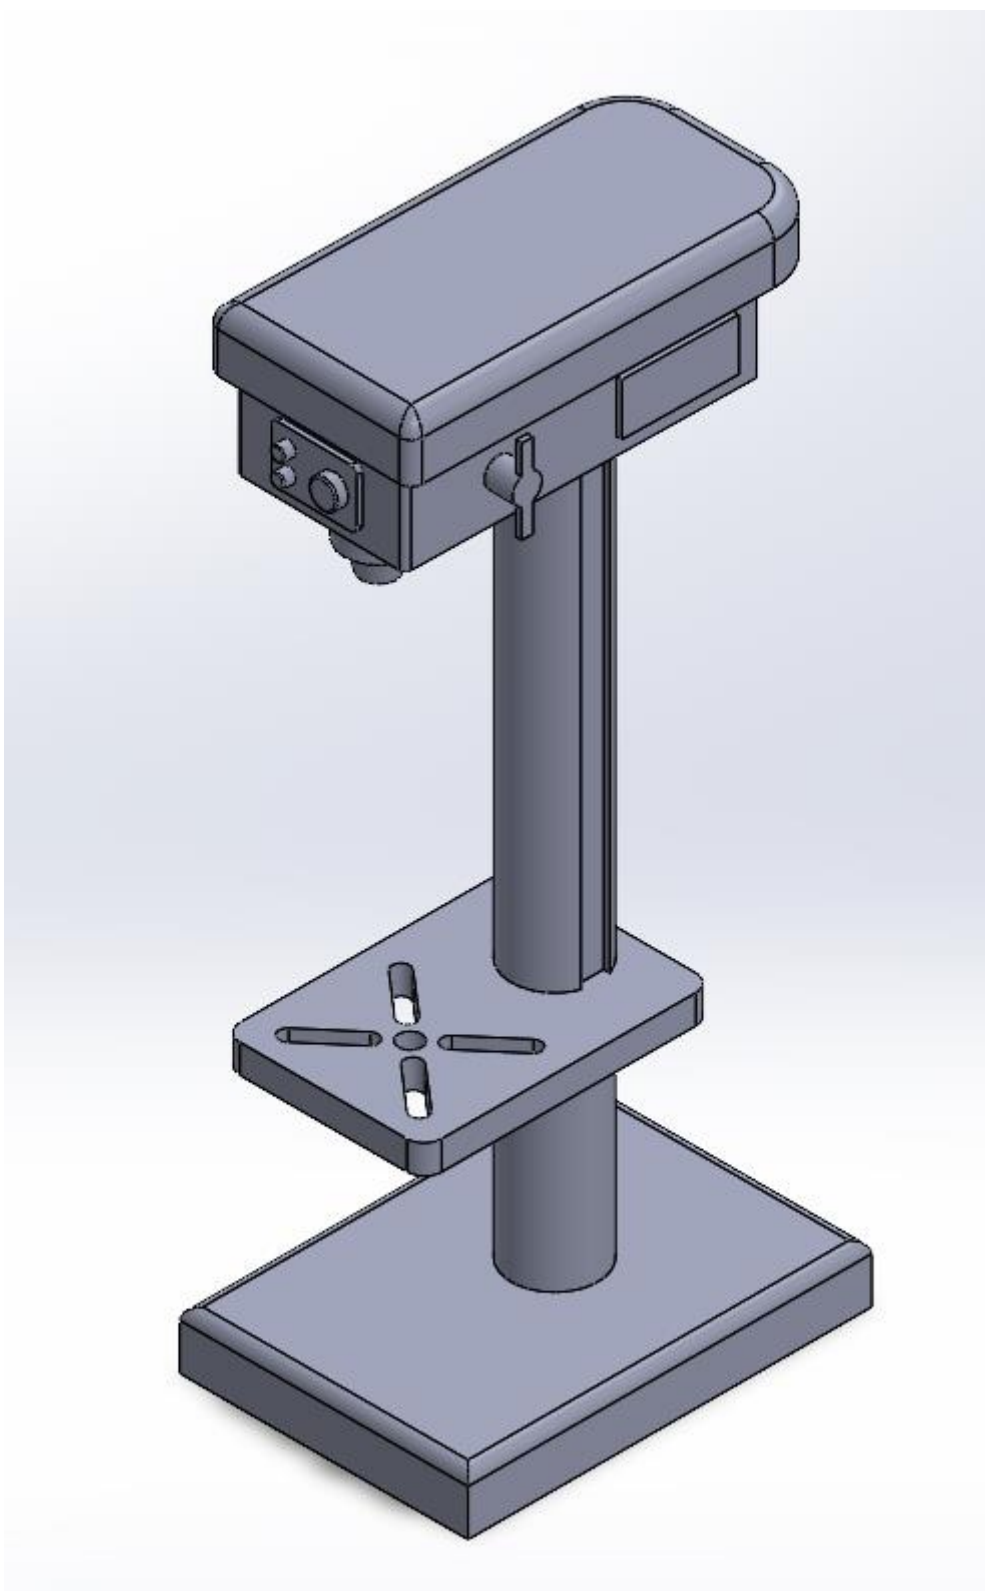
sestava stojanu s vřeteníkem, frézka
